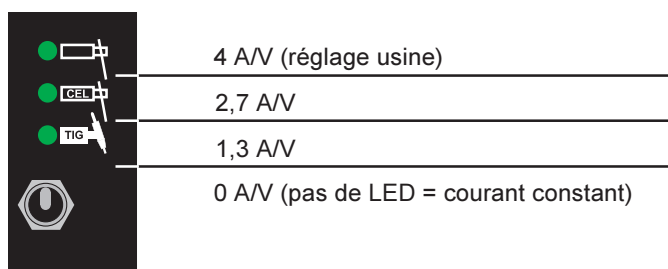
Soudage CEL: réglage du paramètre Caractéristique
